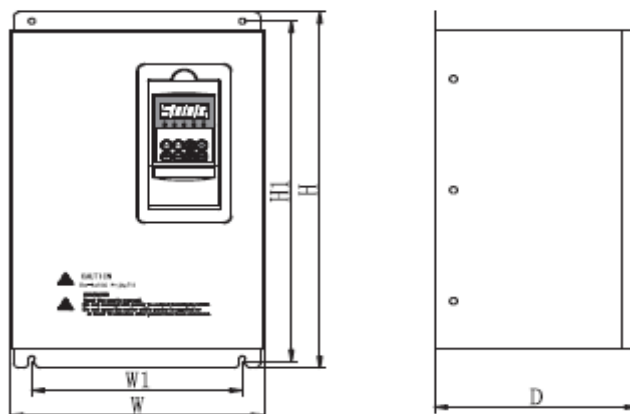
Чертеж с габаритными размерами преобразователя (модель В)
